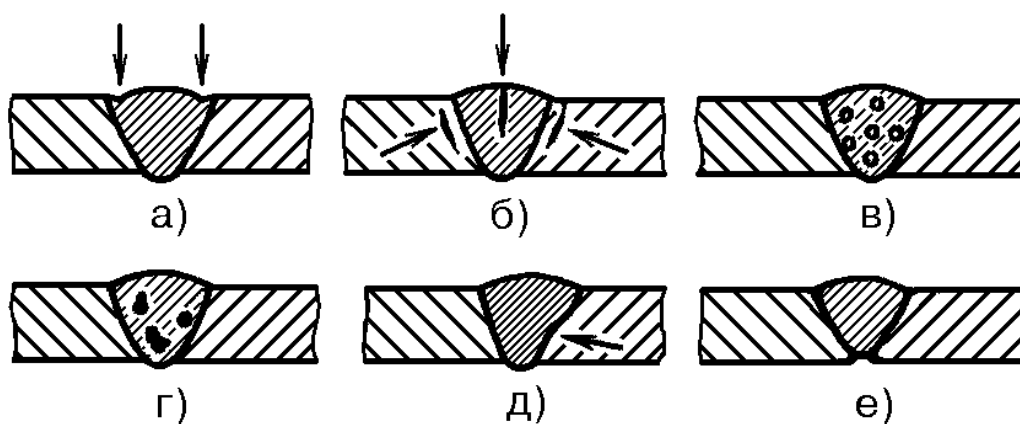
Поперечные сечения сварочных швов с типичными дефектами:
